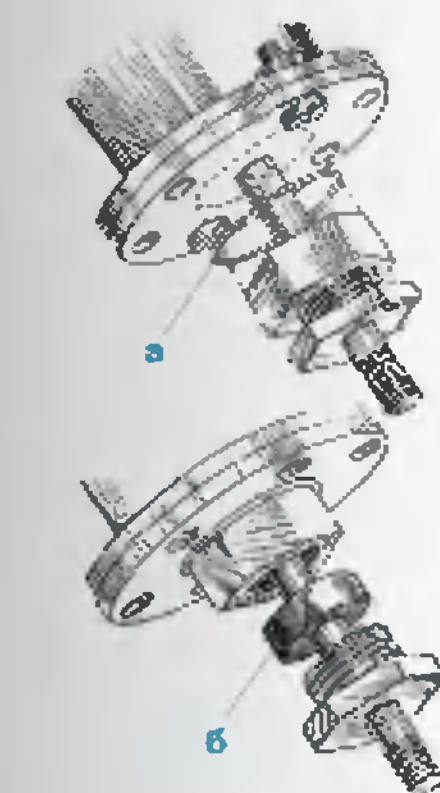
Установка сальника: а) припайка гайки сальника, б) сборка.
